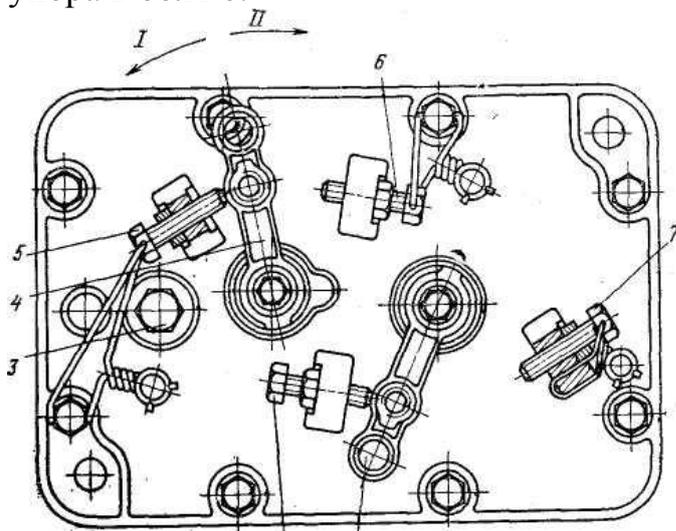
Крышка регулятора с рычагами подачи топлива и останова двигателя:
